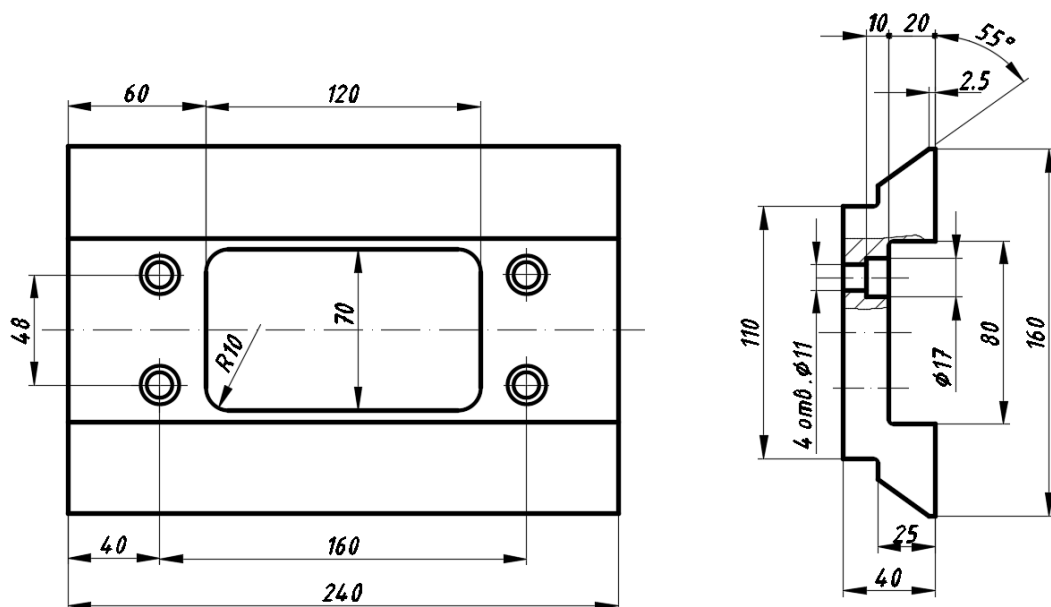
Образец выполнения чертежа детали каретки с направляющими типа «ласточкина хвоста».
